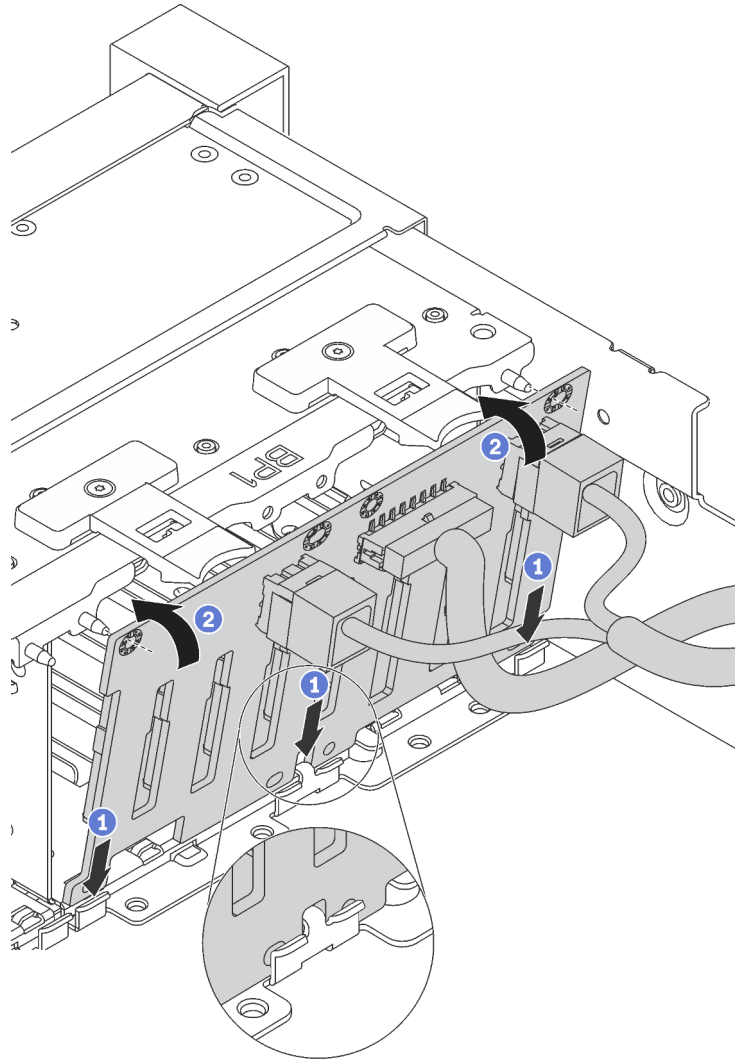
Installation d'un fond de panier d'unité 2,5 pouces
